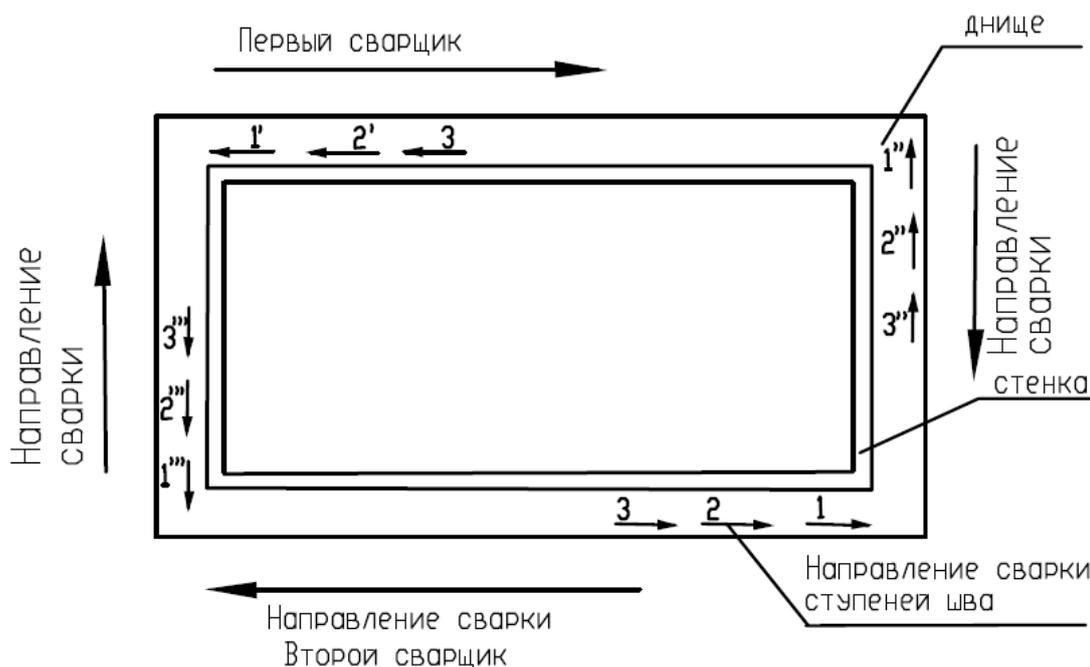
Последовательность сварки соединений прямоугольных конструкций.
